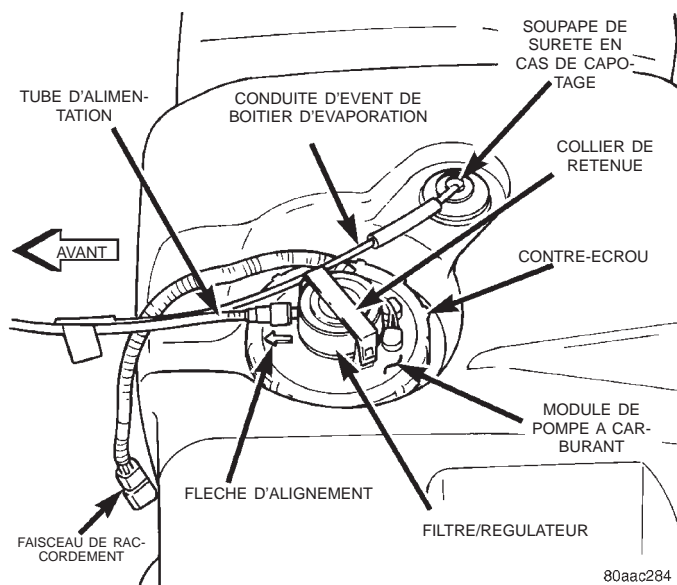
Réservoir/module de pompe à carburant (vus du haut)
